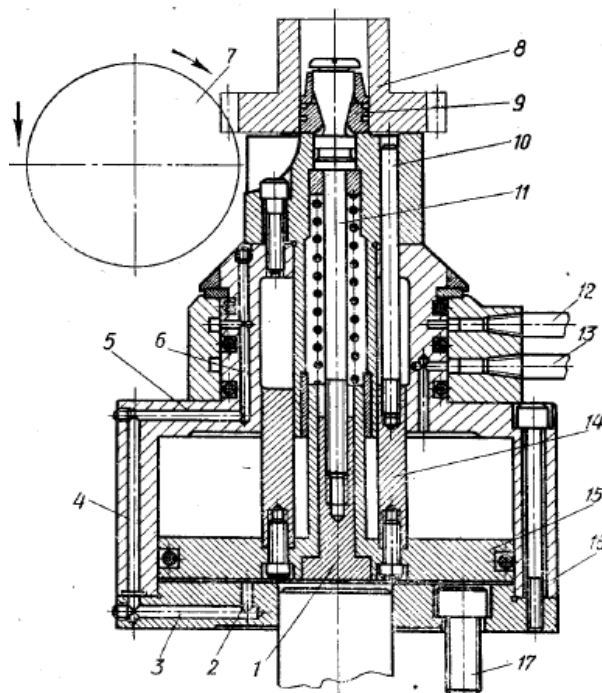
Пристосування з поршневим пневмоприводом для фрезерування зуб'їв циліндричного колеса
